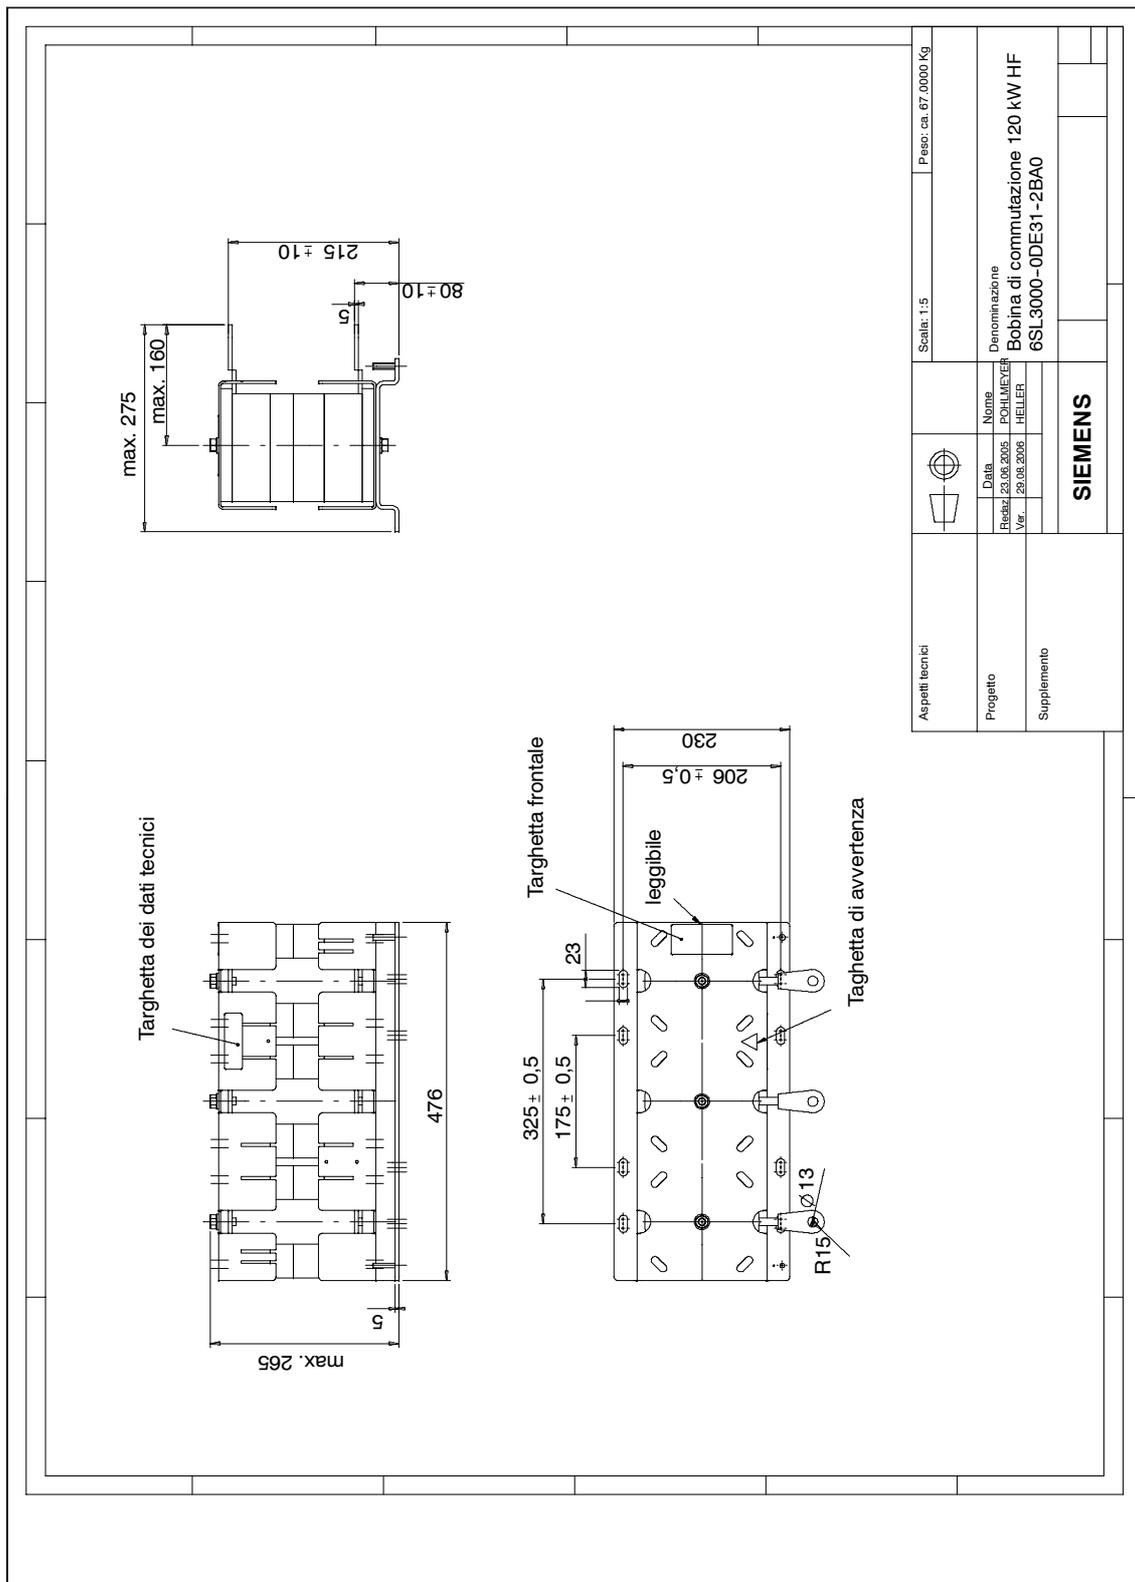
Bobina HF trifase 120 kW, 6SL3000-0DE31-2BAx
